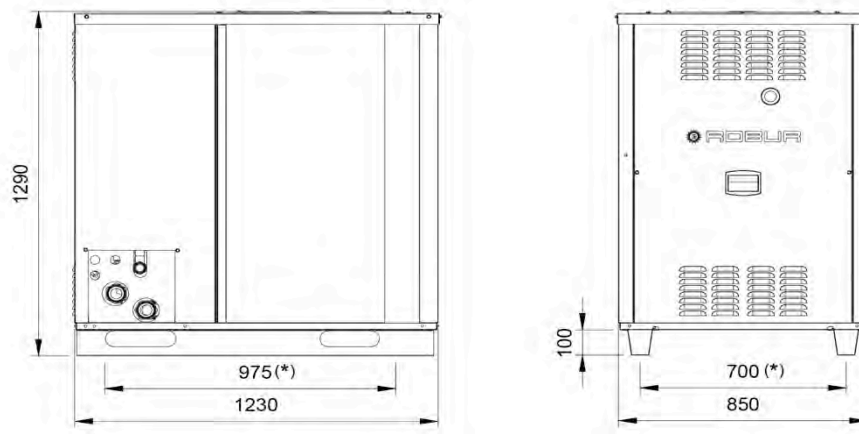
Dimensiones exteriores de la máquina de refrigeración ACF 60-00 (expresadas en mm).
